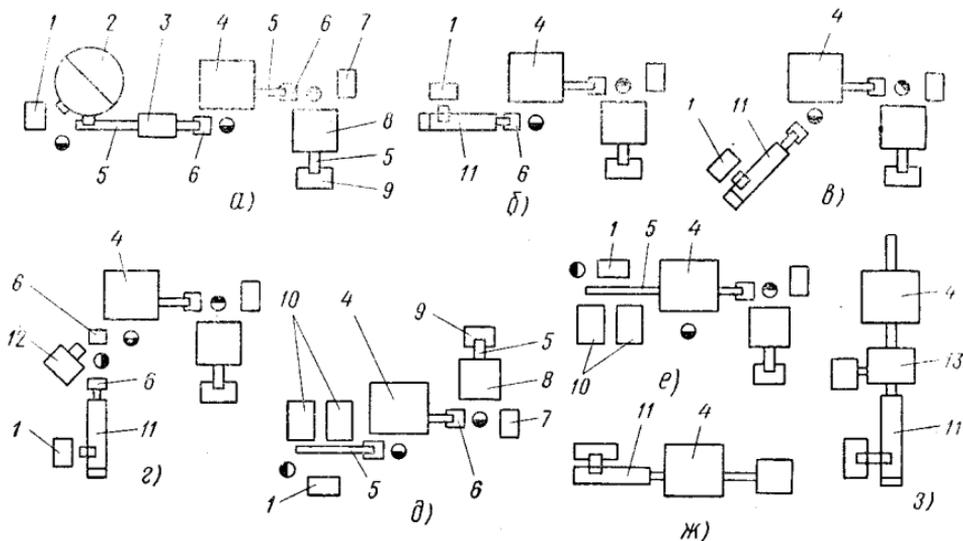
Варианты расположения оборудования на участке кривошипного горячештамповочного пресса:
